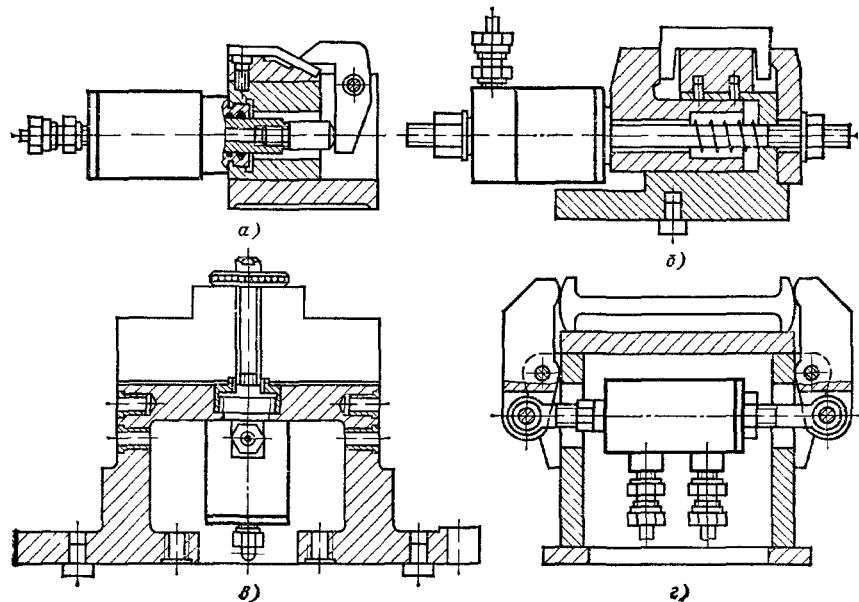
Примеры применения стандартных гидроцилиндров для станочных приспособлений:
